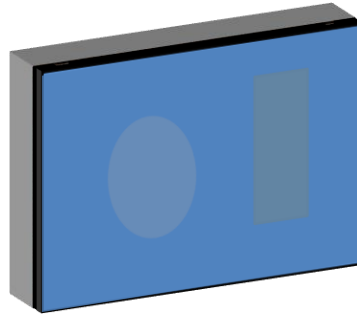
Éprouvette assemblée pour examen des points de collage
